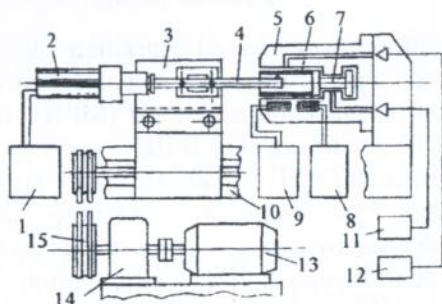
Схема токарного верстата для віброрезітаційного точіння
